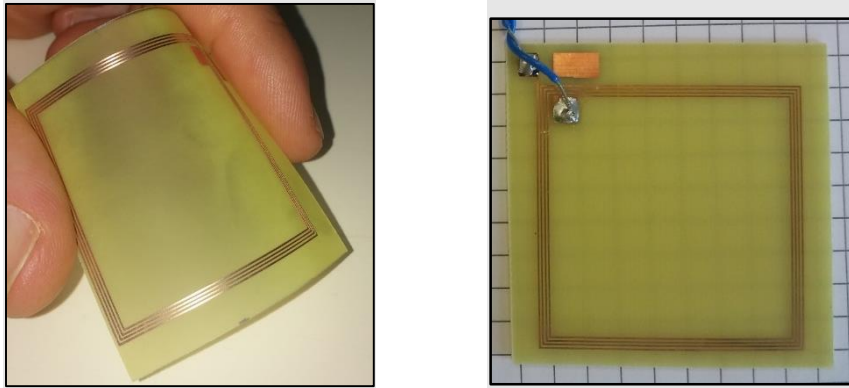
PCB de la bobine réalisée à la graveuse chimique.
